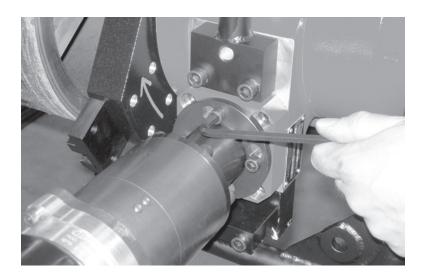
Поверните фланец для посадки винтов в пазах и затяните винты.
